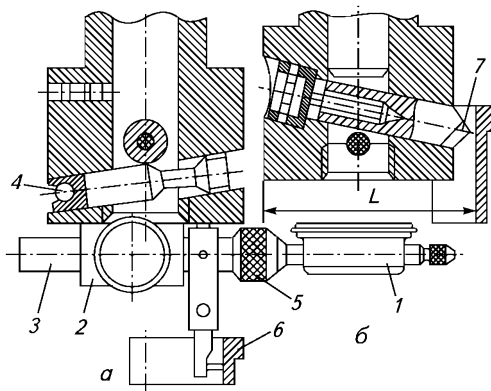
Резцовая головка с приспособлением для центрирования гильз (*а*) и установки резца (*б*):
